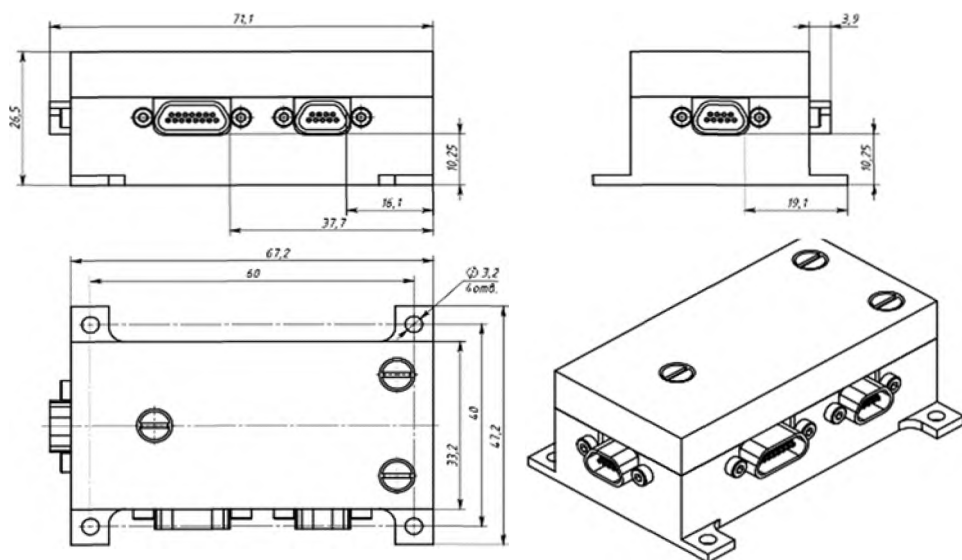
Габаритный чертёж блока управления электромагнитными устройствами SX-MTCU-01
